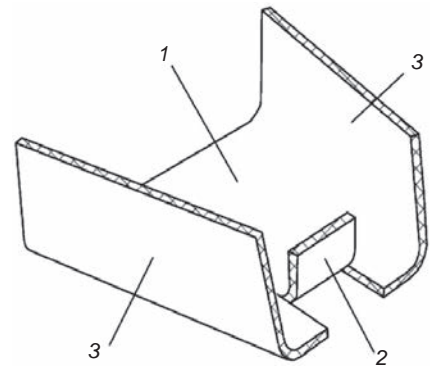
Опорный башмак: 1 – основа; 2 и 3 – упоры.
